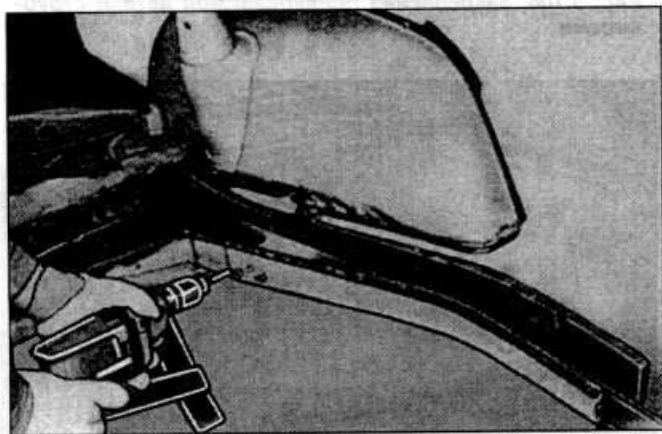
Высверливание сварных точек заднего лонжерона
